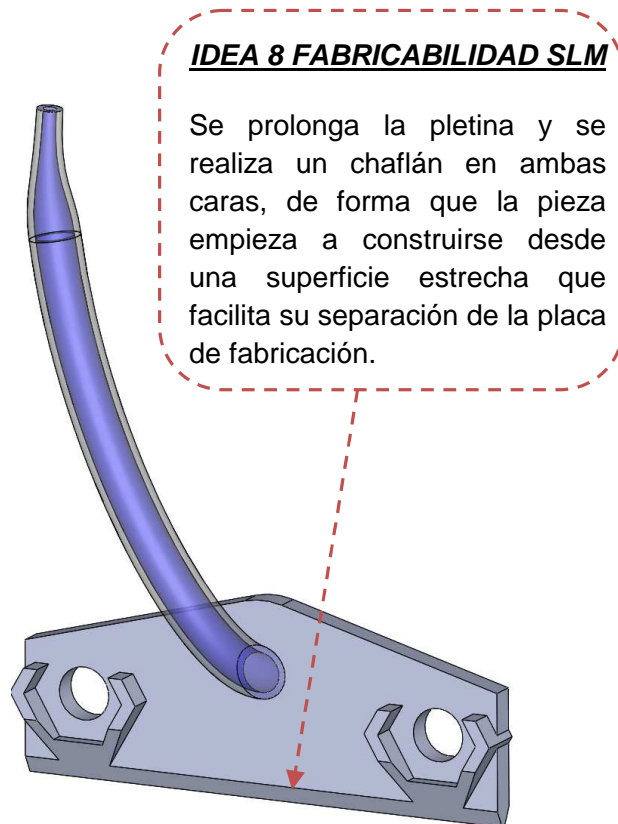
Diseño de detalle del componente con geometría en chaflán para facilitar fabricación y separación de la placa.
